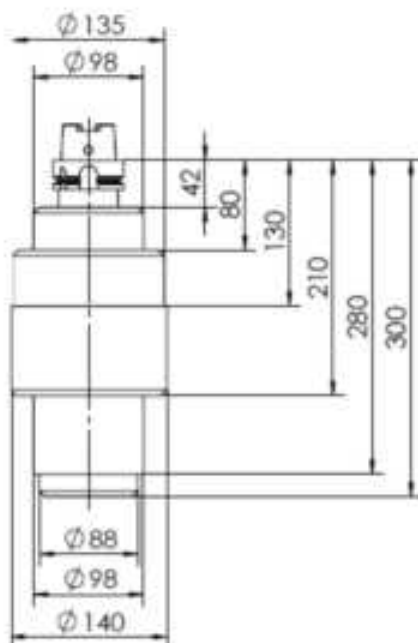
Werkzeugabmessungen bei freien Nebenplätzen
